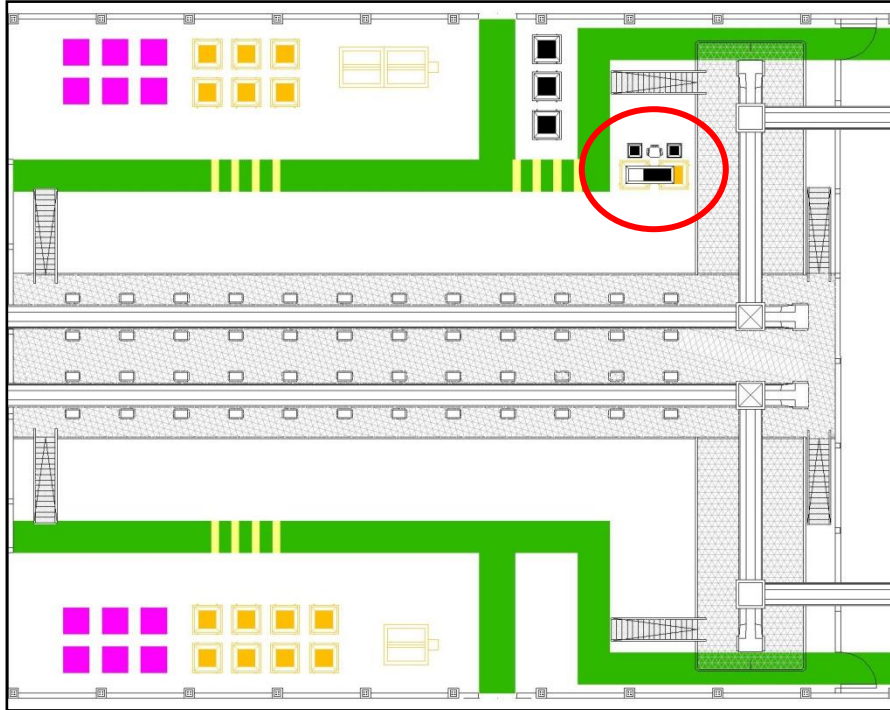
Ubicación de la zona de desetiquetado dentro de la planta.
